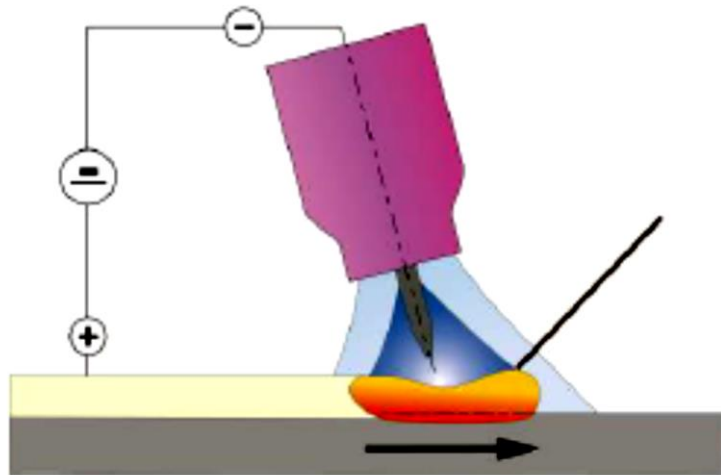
Схема способу ручного аргано-дугового зварювання
